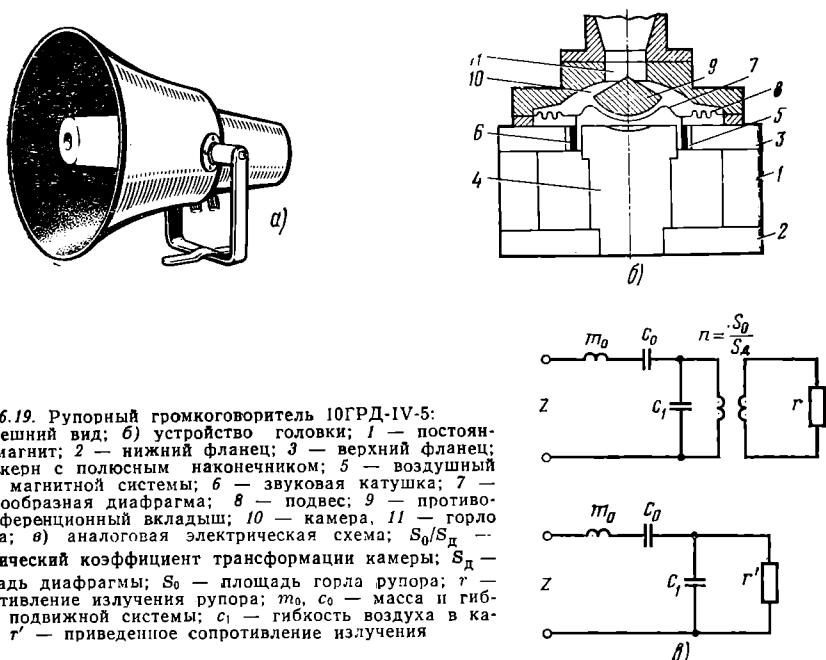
Рупорный громкоговоритель 10ГРД-IV-5: а) внешний вид; б) устройство головки; 1 — постоянный магнит; 2 — нижний фланец; 3 — верхний фланец; 4 — Kern с полюсным наконечником; 5 — воздушный зазор магнитной системы; 6 — звуковая катушка; 7 — куполообразная диафрагма; 8 — подвес; 9 — противоинтерференционный вкладыш; 10 — камера; 11 — горло рупора; в) аналоговая электрическая схема; S_0/S_d — акустический коэффициент трансформации камеры; S_d — площадь диафрагмы; S_0 — площадь горла рупора; r — сопротивление излучения рупора; m_0, c_0 — масса и гибкость подвижной системы; c_1 — гибкость воздуха в камере; r' — приведенное сопротивление излучения
